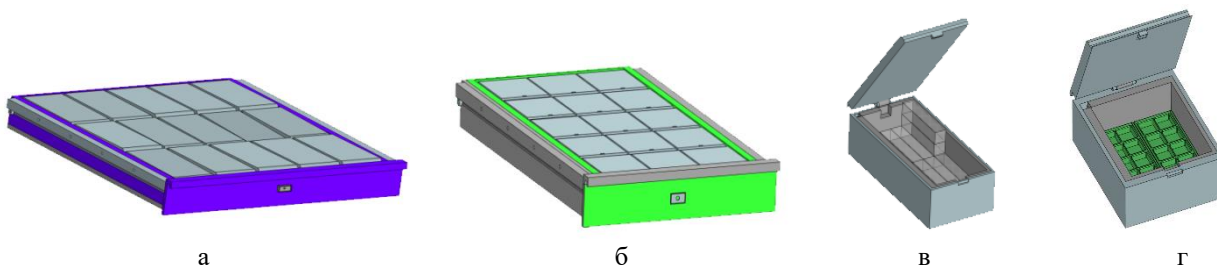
Модели и внешний вид ящиков и ячеек: а – ящик для ячеек с режущим инструментом; б – ящик для ячеек со сменными пластинами; в – ячейка для режущего инструмента; г – ячейка для сменных пластин
